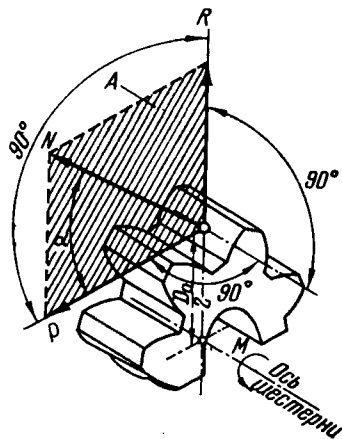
Схема цилиндрической шестерни с прямыми зубьями и сил, действующих в точке контакта.
